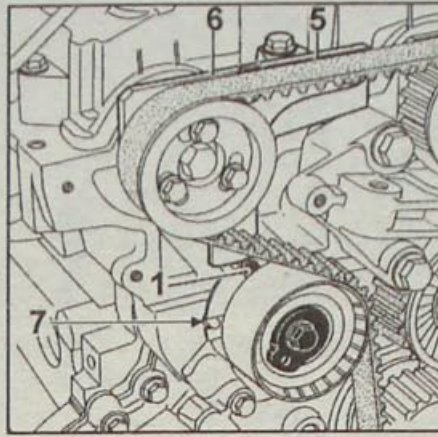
Установка ремня привода газораспределительного механизма:
